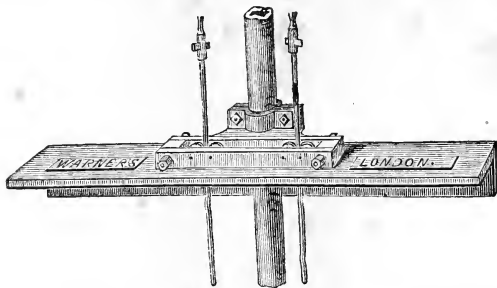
Guide des tringles de piston, dans une pompe à deux corps.
